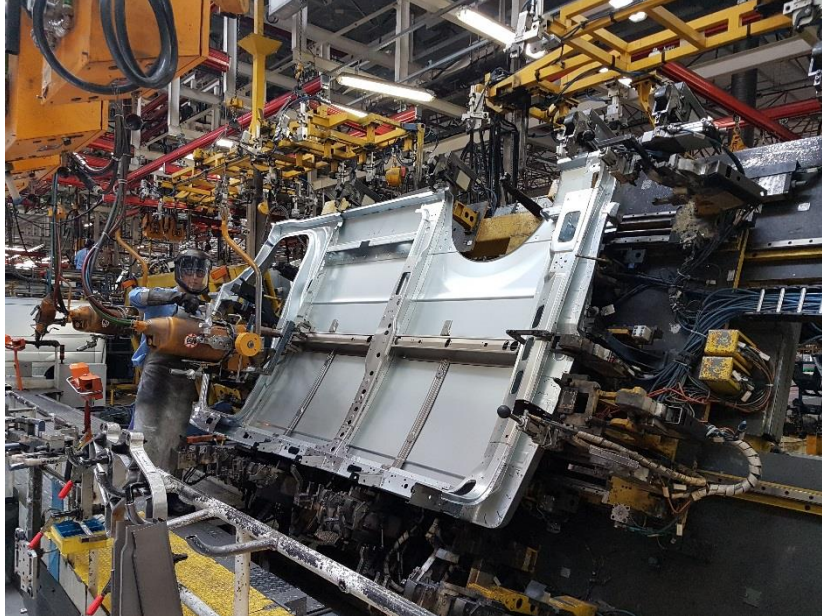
Soldagem de Componentes em um Modelo X3 no Posto G02.
